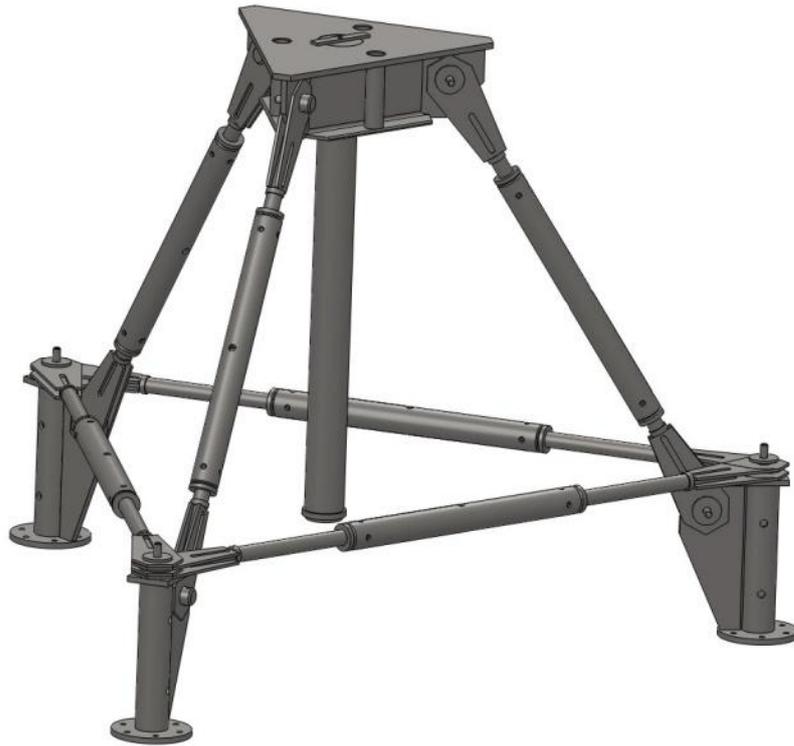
Схема УУ-ВСК для испытания на вдавливание
